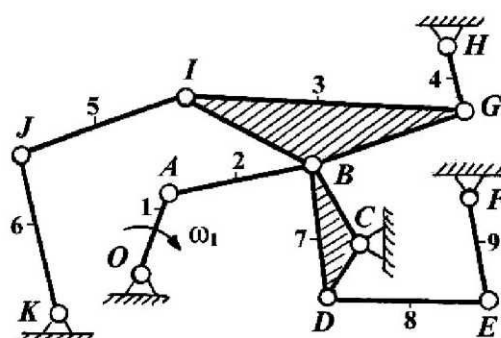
Механизм очистки зерноуборочного комбайна
